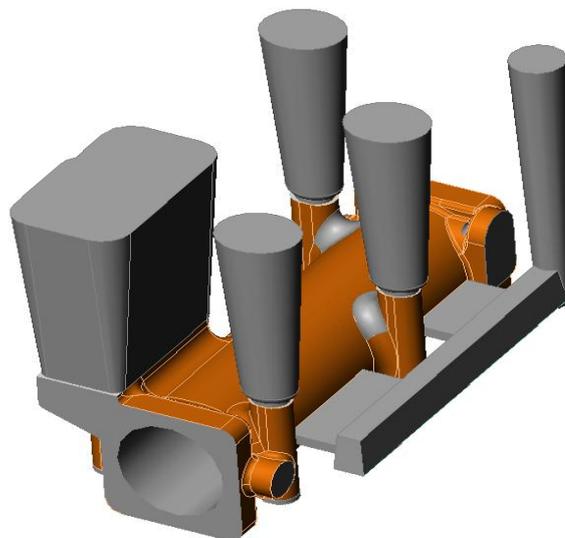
Трёхмерные модели отливки с литниково-питающей системой
